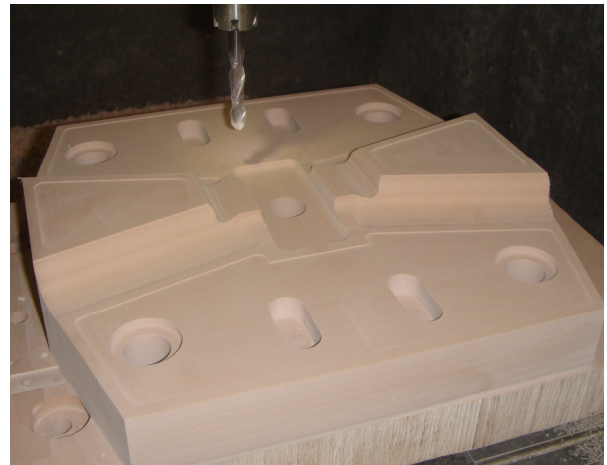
Výroba hornej dosky- operácia rest milling- 10V
